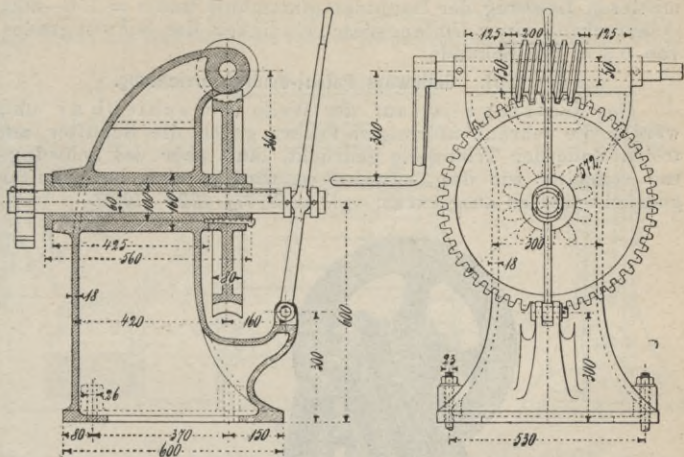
1028. Ausrückung mit Hebel on Hand.
